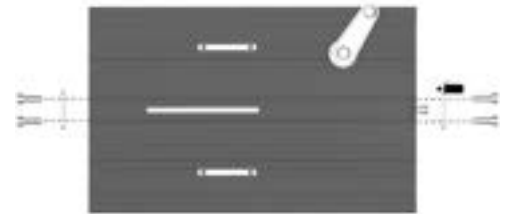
Die Halterungen der Einstellleiste sind mit jeweils zwei Schrauben befestigt.
